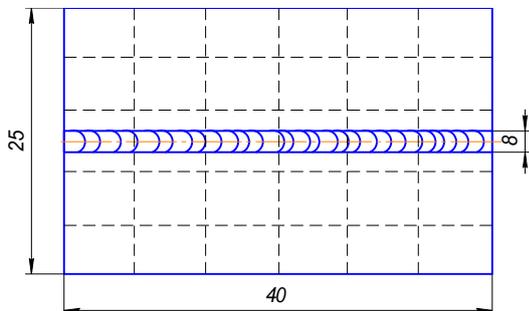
Схема образцов для контроля напряжений в сварном образце
